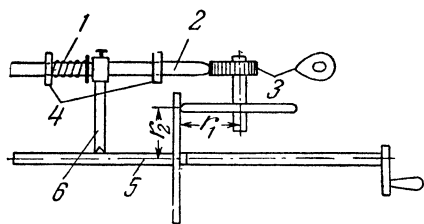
Схема станка для намотки катушек типа «Универсаль».
